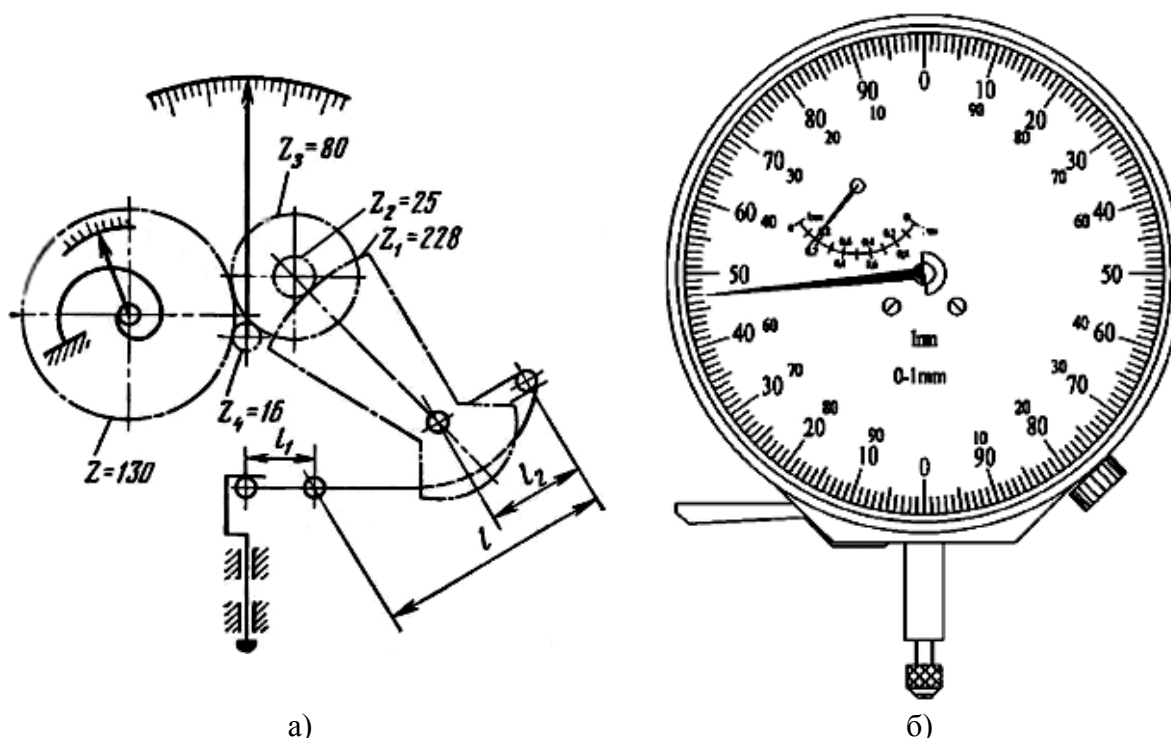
Кинематическая схема и внешний вид многооборотного индикатора 1 МИГ
